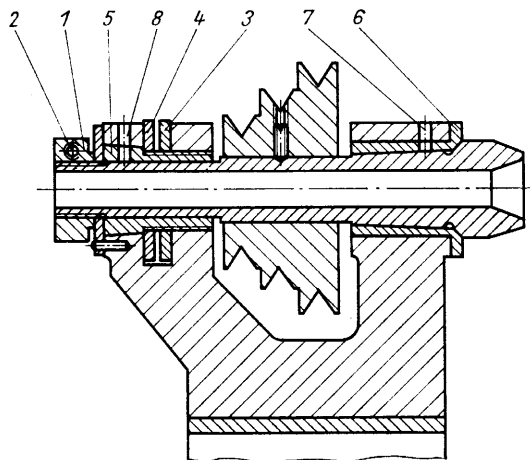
Spindelstock mit kegligzylindrischer Arbeitsspindel
